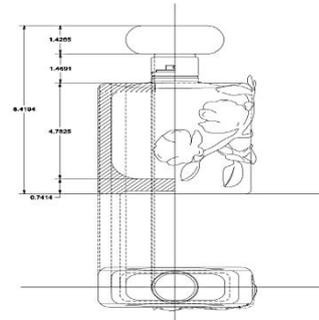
مسقط رأسي وأفقي وقطاع للفكرة التصميمية السادسة
